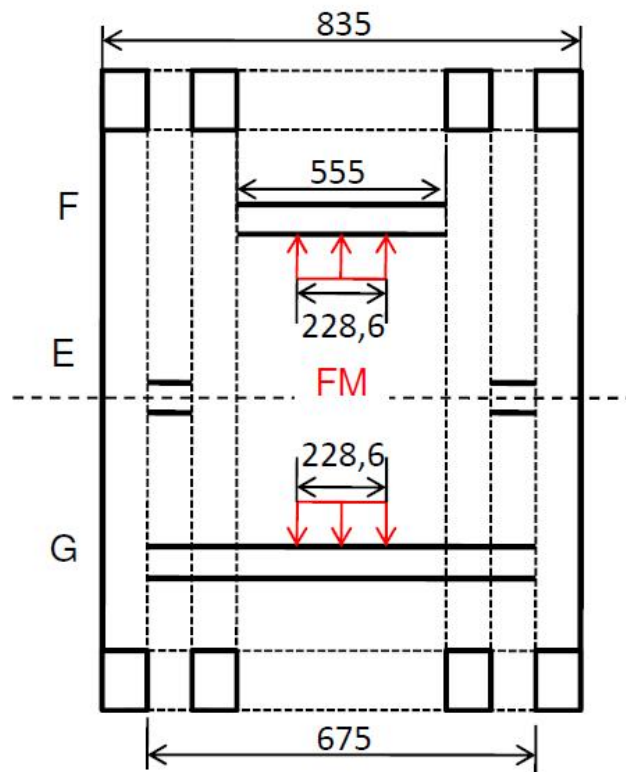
Vista da seção transversal do elevador, diagrama de forças das vigas bi-engastadas.
